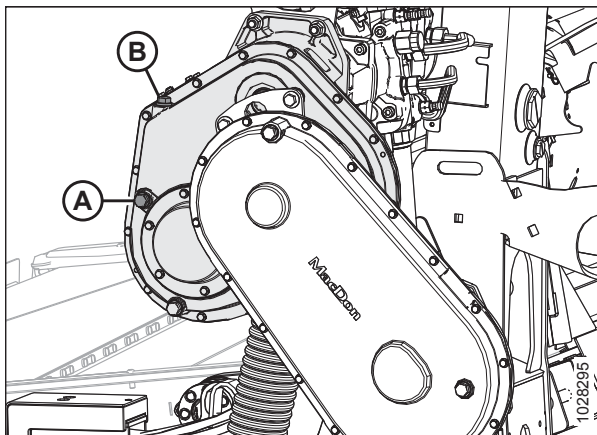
Caja de engranajes principal del mando de la plataforma
